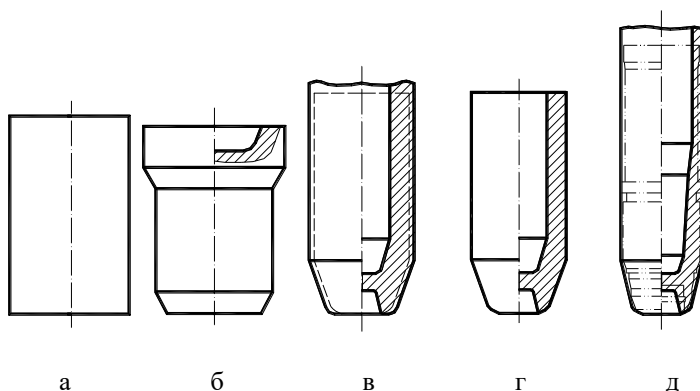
Схема технологического процесса штамповки деталей с глубокой полостью: а – исходная заготовка круглого или квадратного сечения, отрезанная от прутка на пресс-ножницах; б – калибровка с наметкой отверстия; в – прошивка; г – механическая обработка; д – вытяжка с утонением стенки
